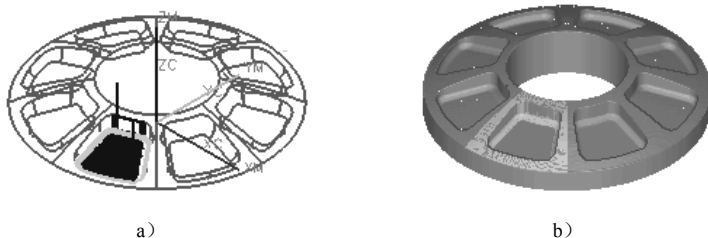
复制等高轮廓铣的“切削刀具路径”和“切削验证”
